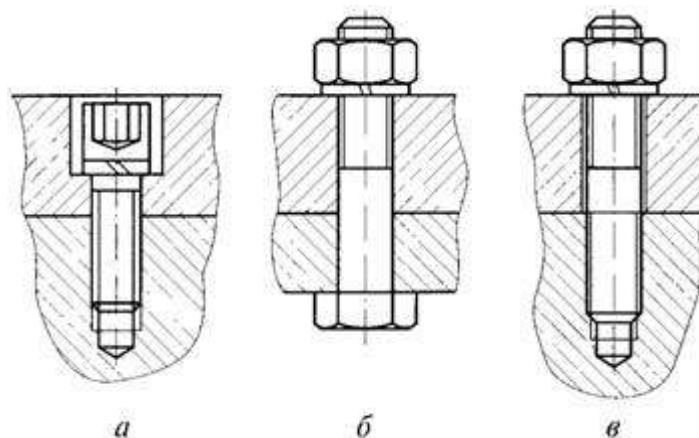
Резьбовые соединения: а) винтовое; б) болтовое; в) шпильчное
